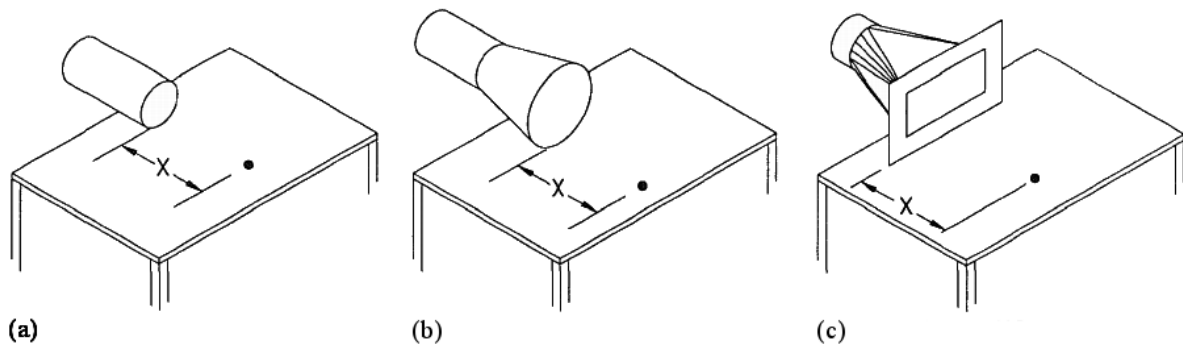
Forma dos captosres para operações de soldagem: (a) captor de abertura plana circular; (b) captor afunilado circular; (c) captor afunilado retangular com flange
